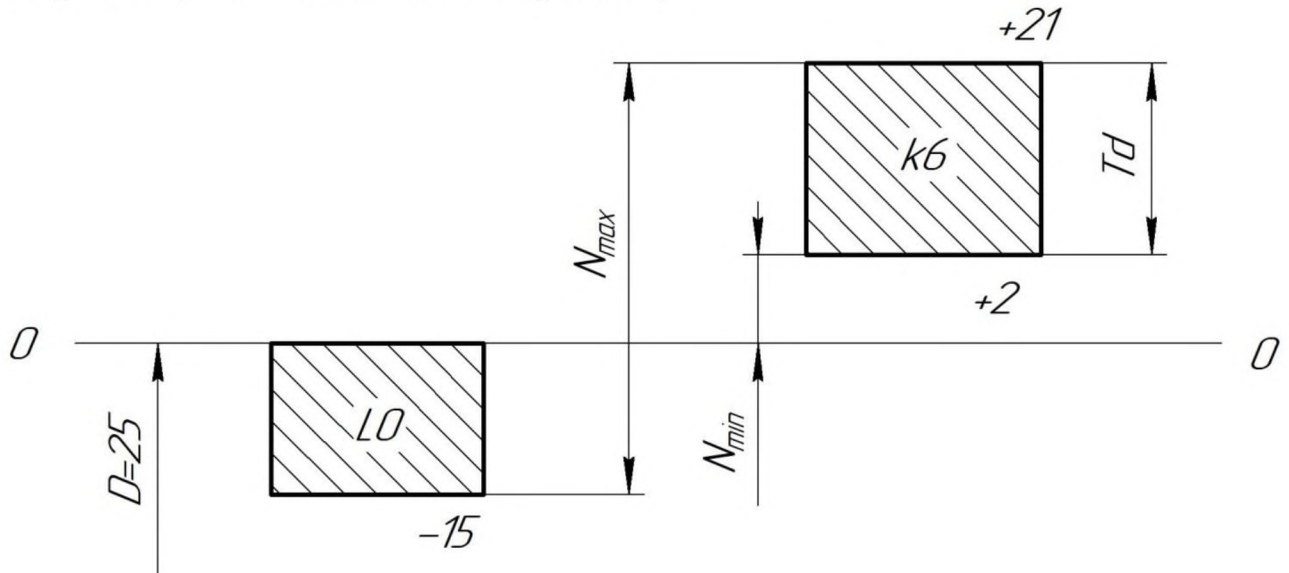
Схема полів допуску підшипника кочення
